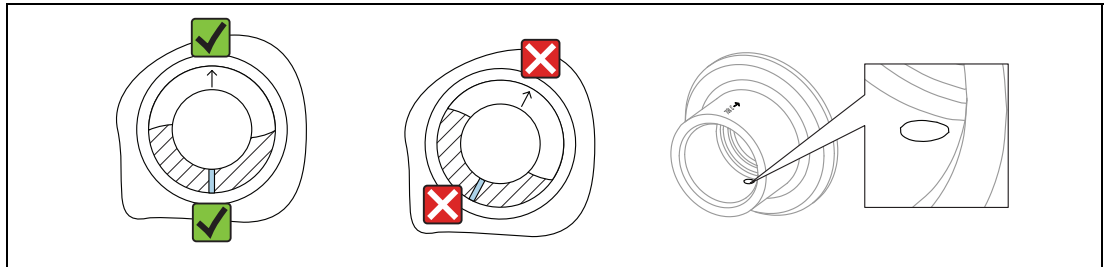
Einschweißadapter mit Leckagebohrung
